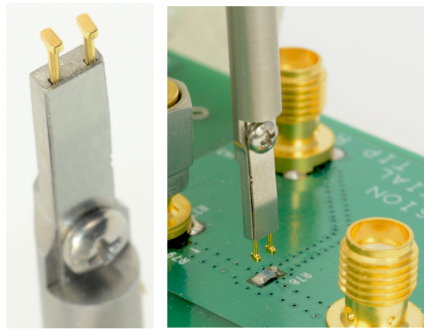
Utilisation de l'outil d'aide à la soudure pour installer les broches carrées sur le circuit imprimé
